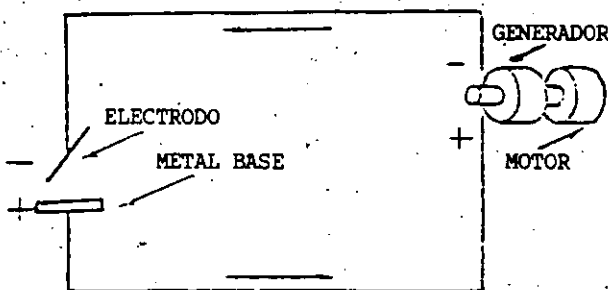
FIG. _____ CIRCUITO DE SOLDADURA DE ARCO CON ELECTRODO METALICO.
